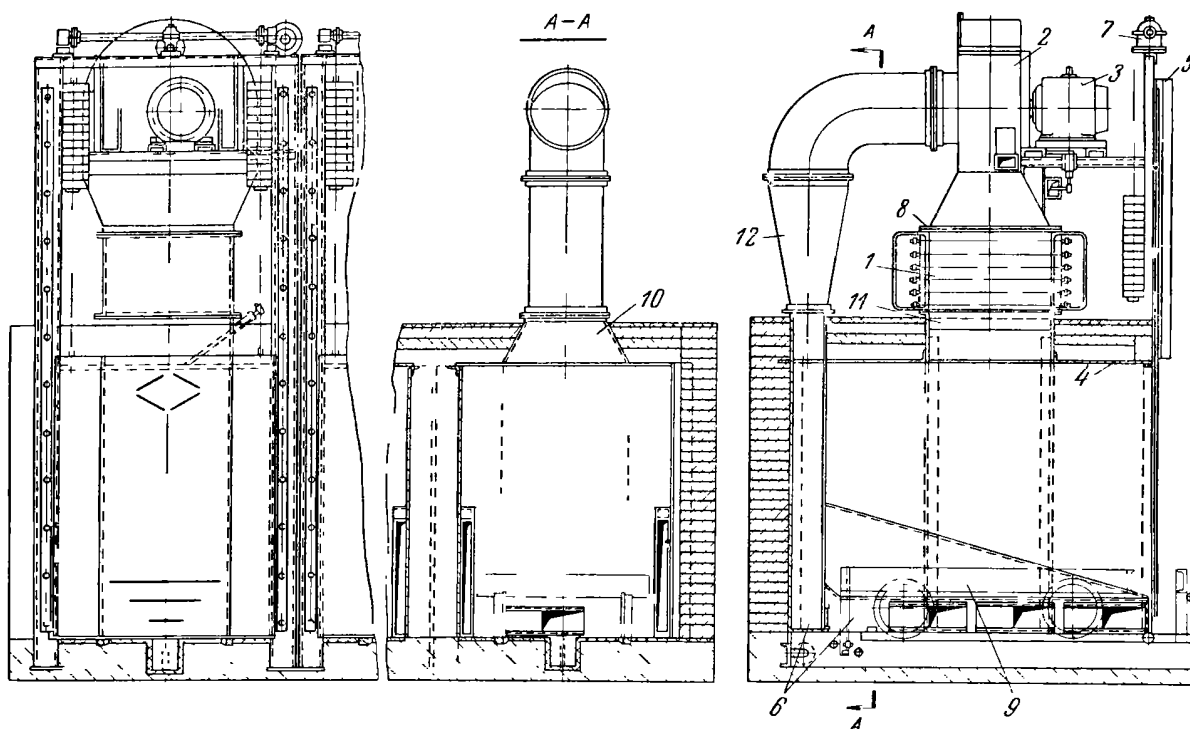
Сушильная печь. 1 – калорифер; 2 – вентилятор; 3 – электродвигатель; 4 – каркас; 5 – дверь; 6 – короб; 7 – механизм подъема двери 8 – прокладка; 9 – тележка; 10 – патрубок вытяжной; 11 – патрубок калорифера; 12 – всасывание воздуха.
